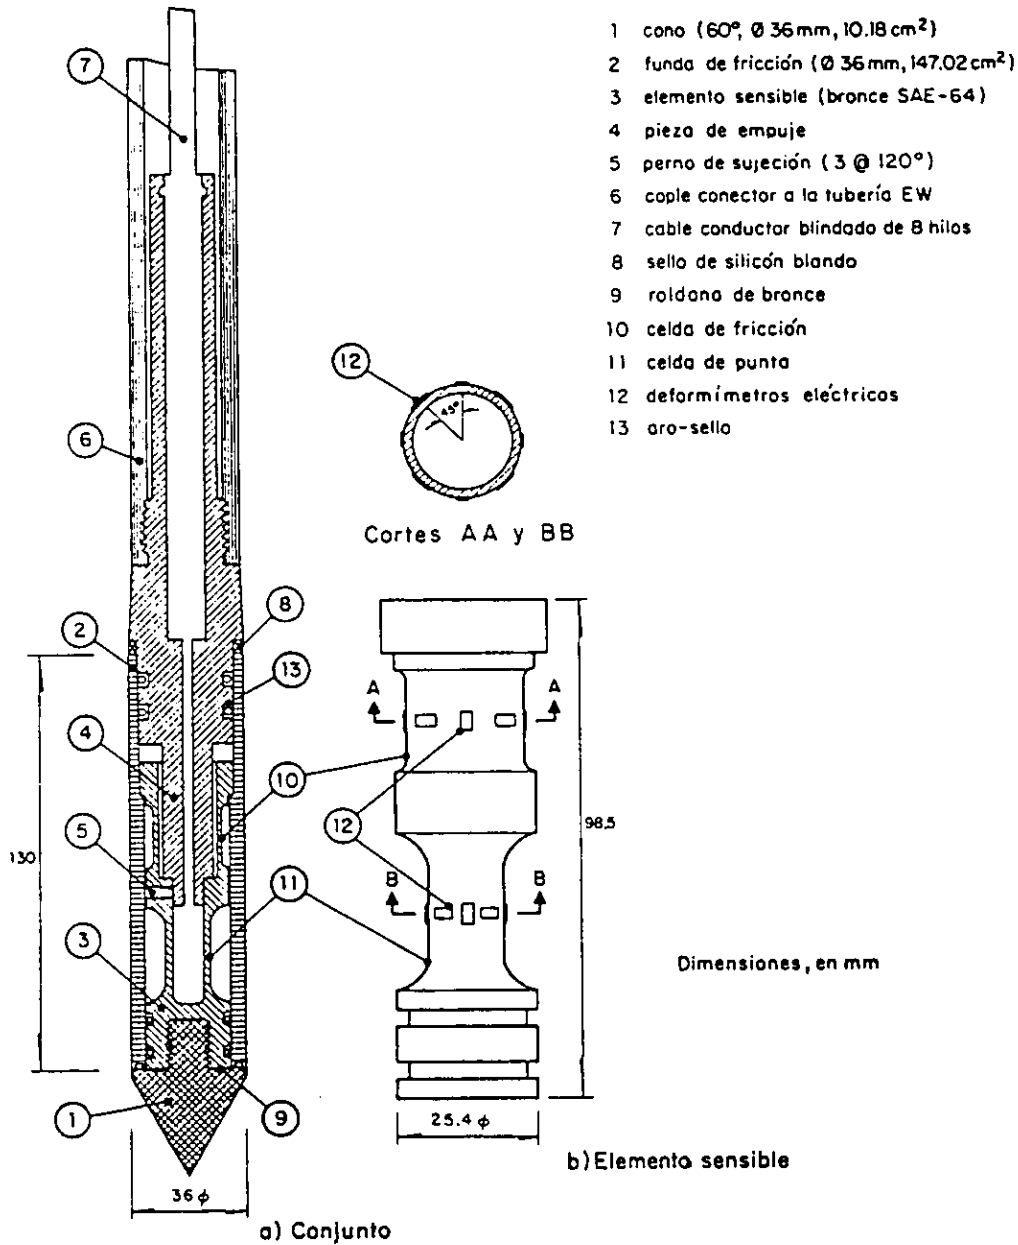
Corte transversal de penetrómetro eléctrico
